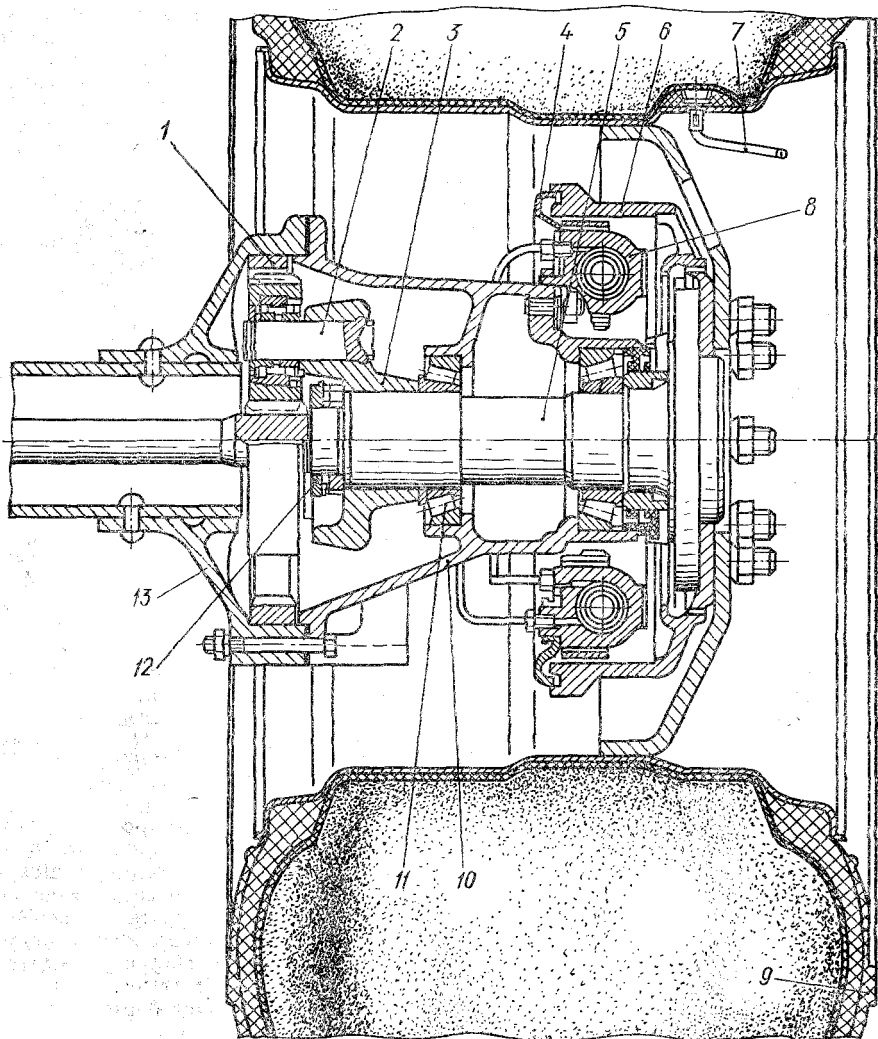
Боровий редуктор, гальмівний барабан та ведуче колесо комбайна СК-5А:
